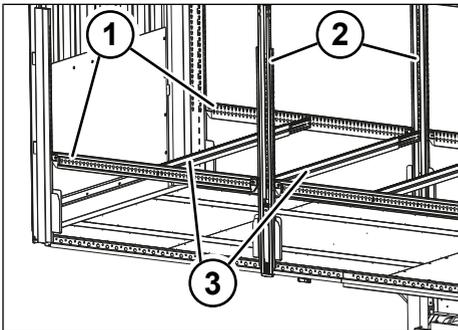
Elementos de suporte para a estrutura de dois andares
